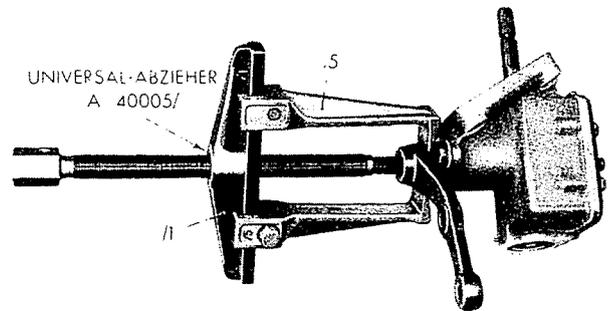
Lenkstockhebel mit Universal-Abzieher A. 40005 1.5 abnehmen.
